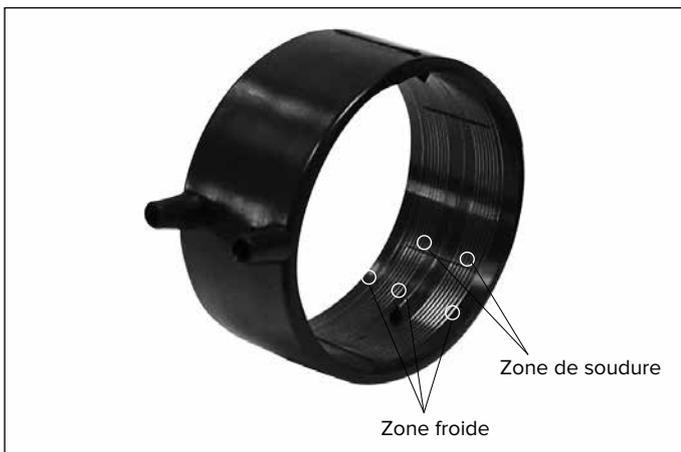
Manchon électrosoudable Akafusion avec zone froide et zone de soudure
